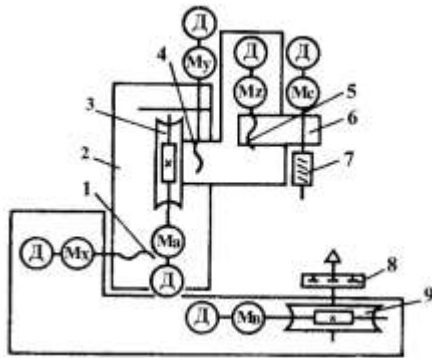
Принципова схема зубофрезерного станка з ЧПУ
